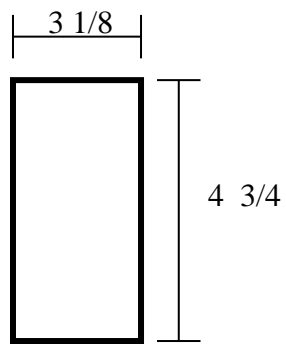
Dimensiones del tubo rectangular empleado en la construcción del soporte fijo
